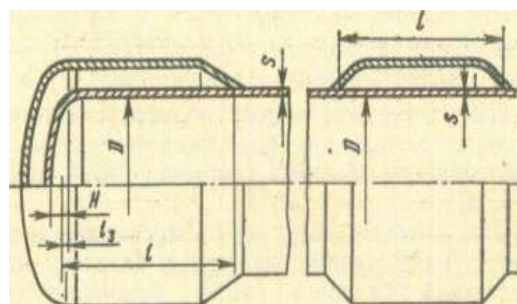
Схема и основные размеры гладкой обечайки с рубашкой
